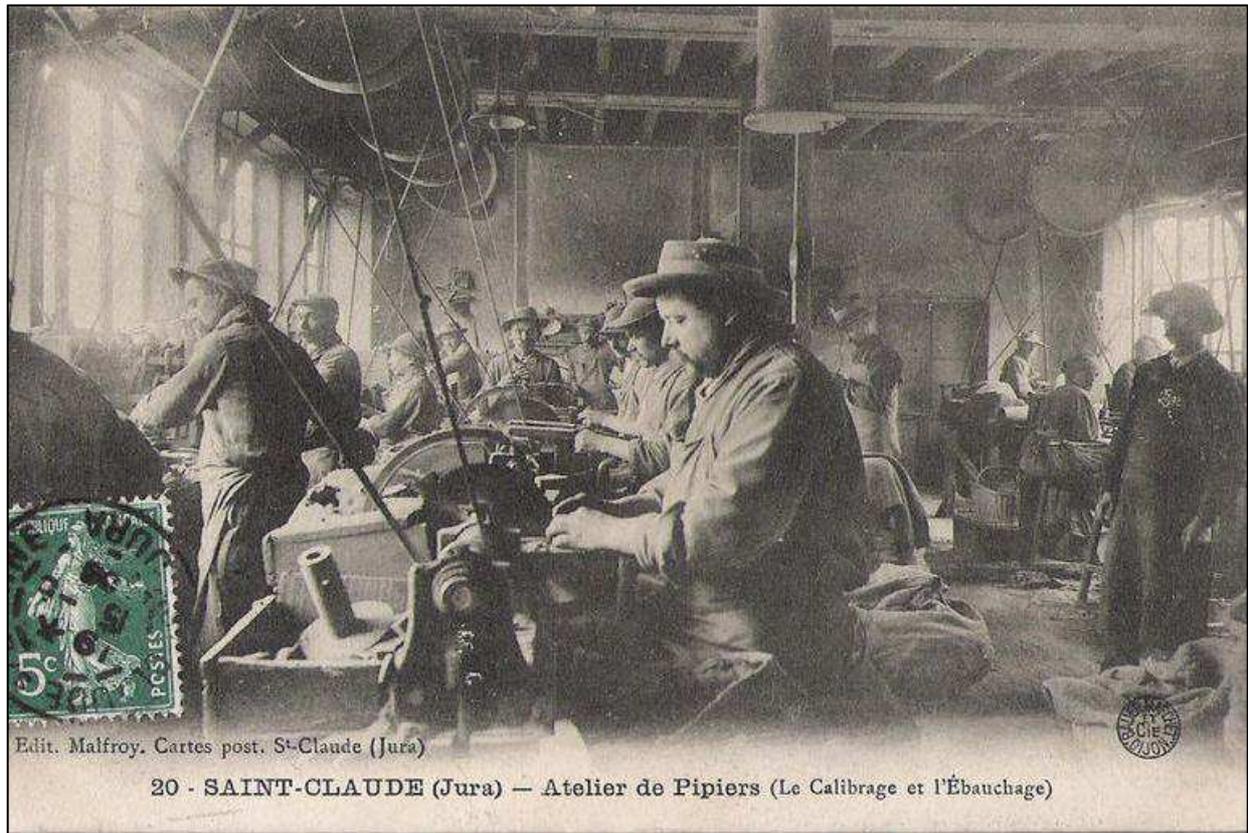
les ateliers de pipiers étaient nombreux dans la ville et ont embauché jusqu'à 4 000 ouvriers (<https://www.actuacity.com/>)
